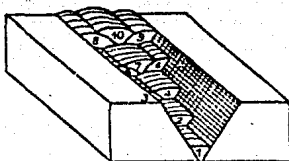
Disposición de los cordones de soldadura en el método por pasadas estrechas.
